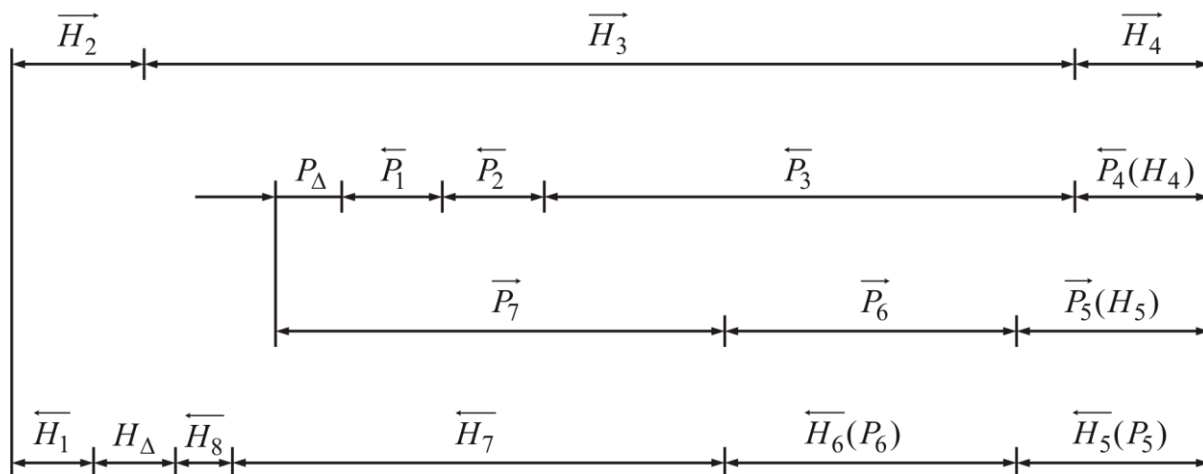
Параллельно связанные размерные цепи вала колеса червячного редуктора
